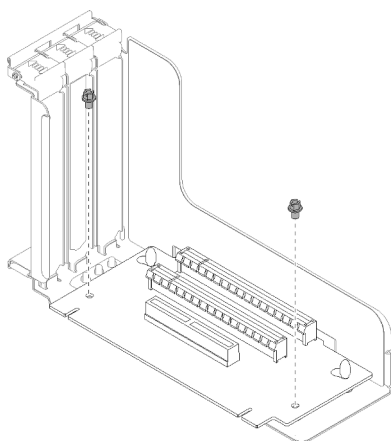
Desensamblaje del conjunto de tarjeta de expansión PCIe
